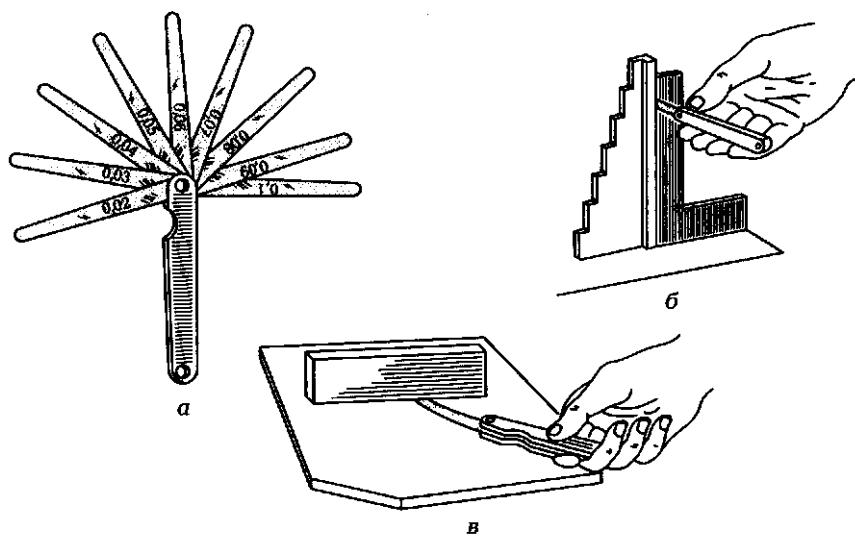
Калибр-щупы и контроль с помощью щупов:
